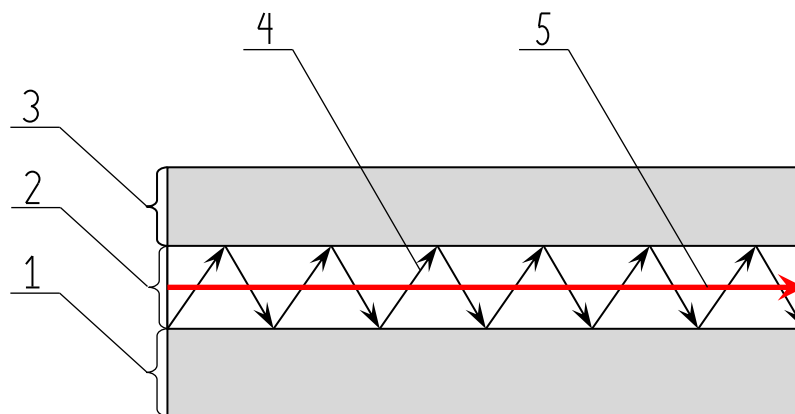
Структура зварного з'єднання та напрямки руху електроду
